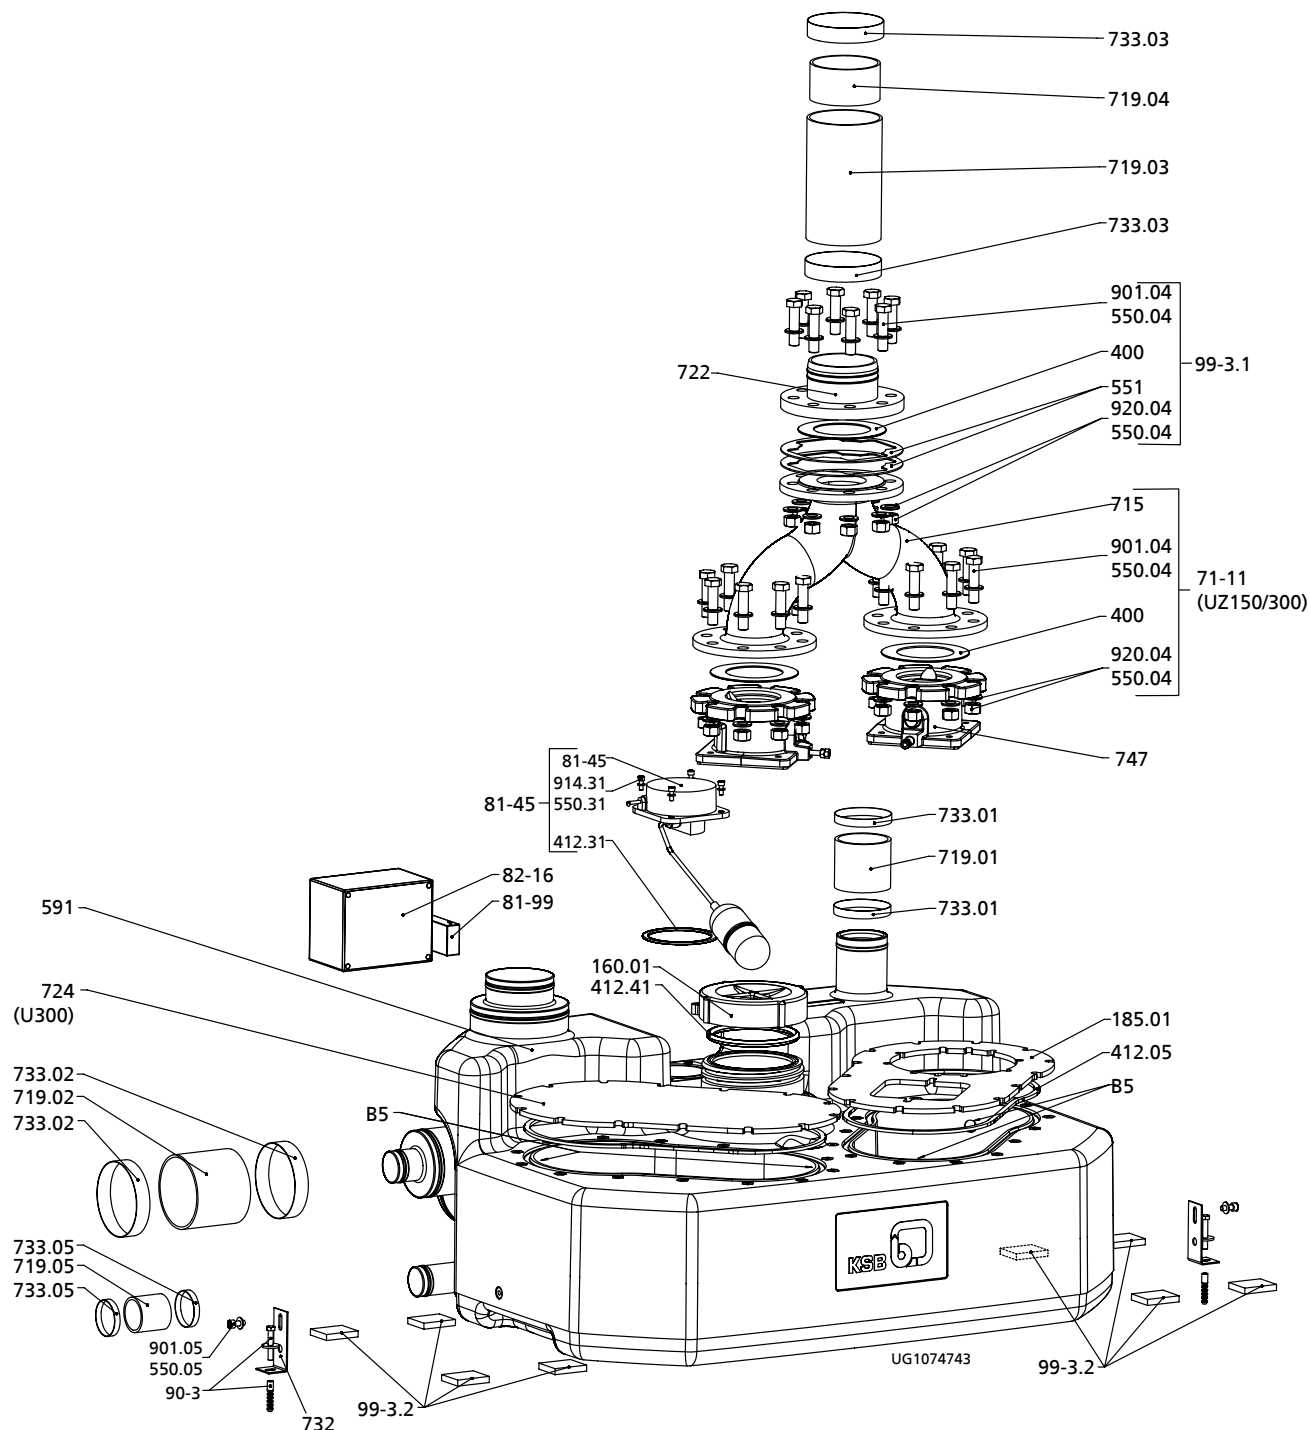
Покомпонентный сборочный чертеж Комплекта UZ150, U/UZ300 – резервуар
